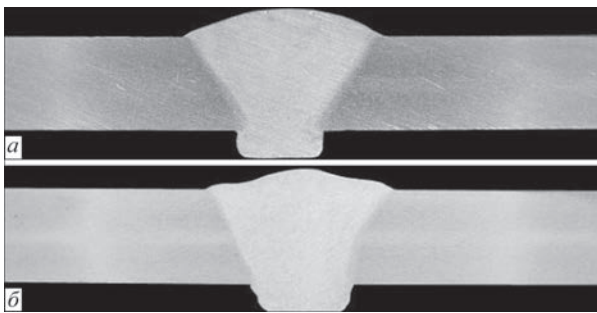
Поперечные шлифы сварных соединений алюминиевого сплава 5083 толщиной 8 мм, полученные сваркой плавящимся электродом (а) на скорости 5 мм/с и гибридной плазменно-дуговой сваркой (б) плавящимся электродом
